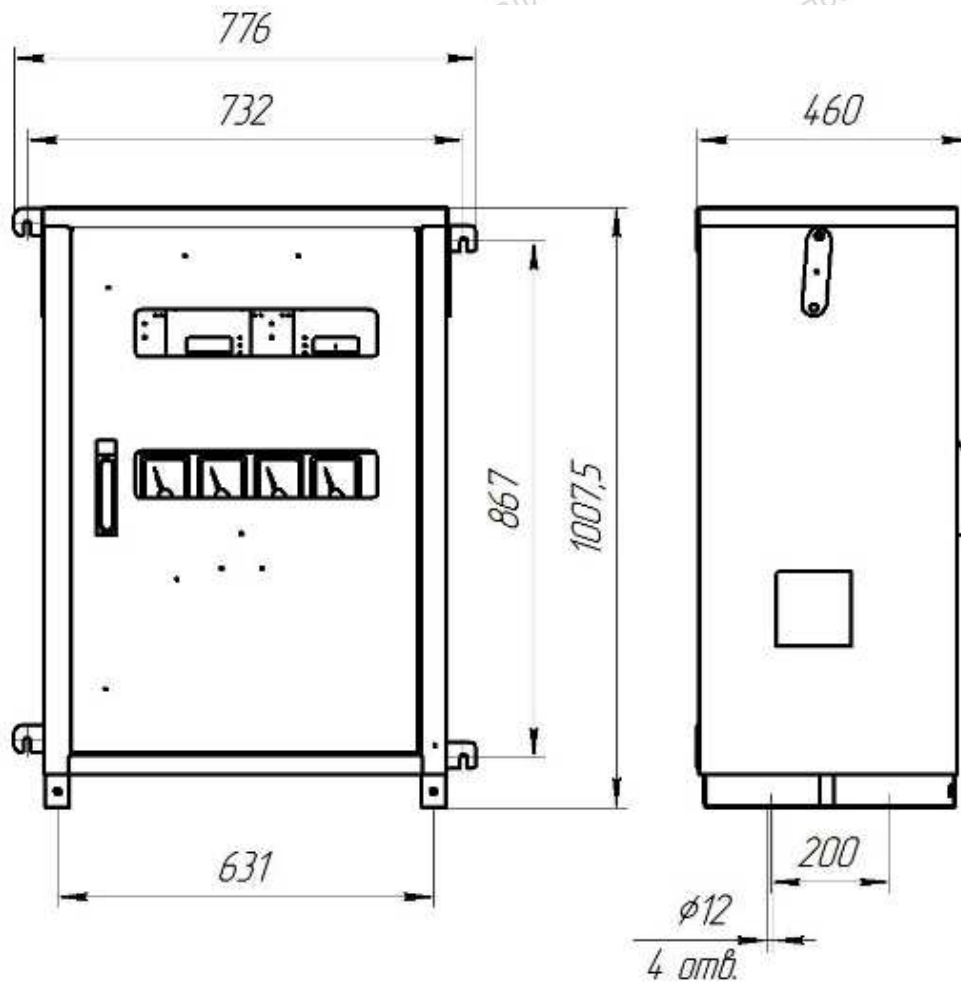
Габаритные, установочные размеры ИСКЗ
